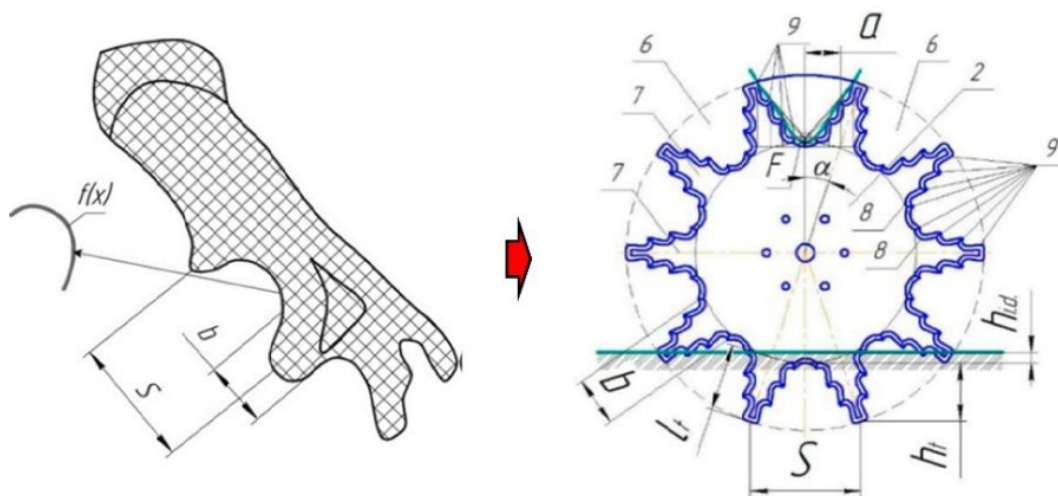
Конструкція робочих органів культиватора на основі поворотних дисків із зубами на основі кінцівки жука-носорога
